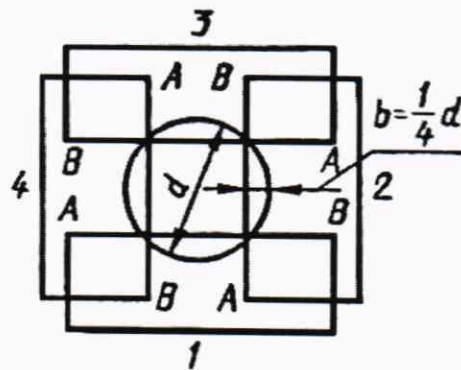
Установка концевых мер между измерительными поверхностями толщиномера
